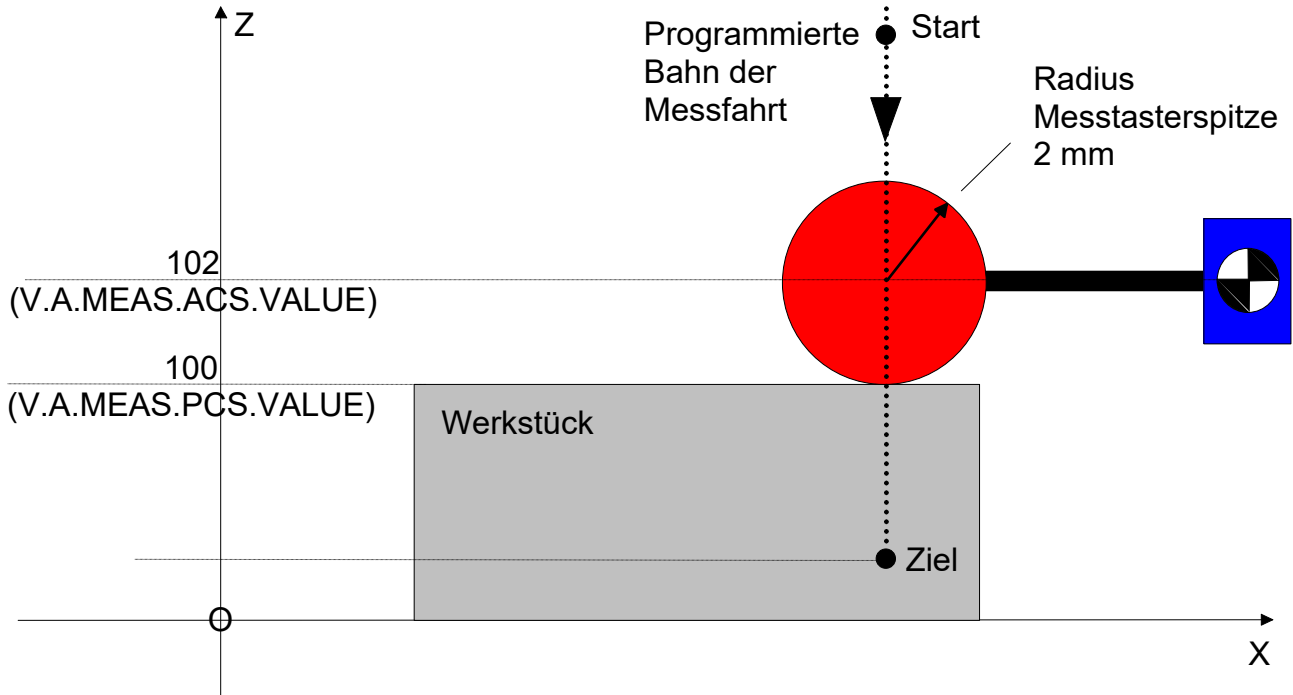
Messen mit einem Messtasterwerkzeug mit 2mm Radius
